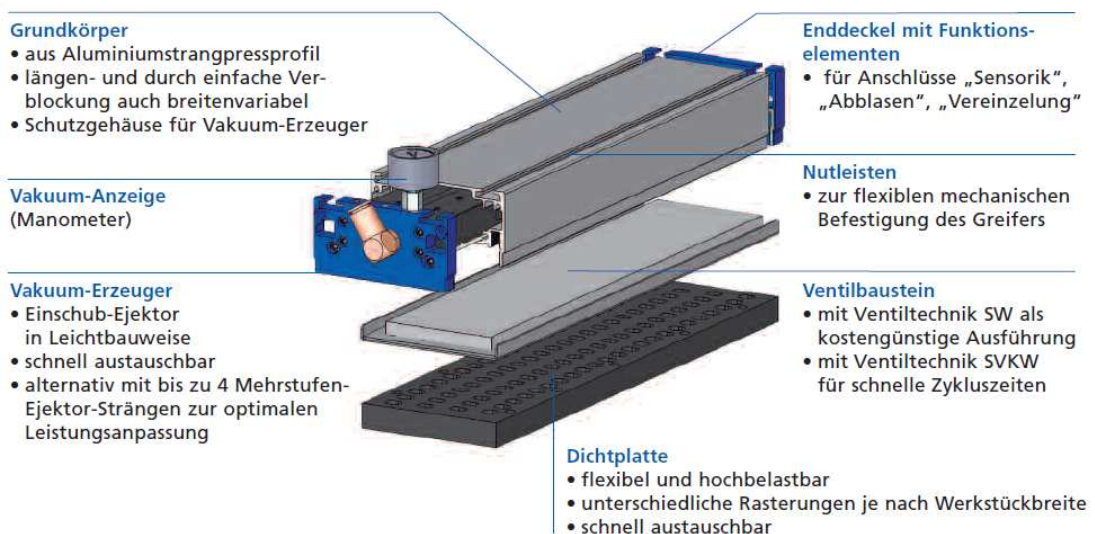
Flächengreifsystem mit integriertem Vakuum Erzeuger
